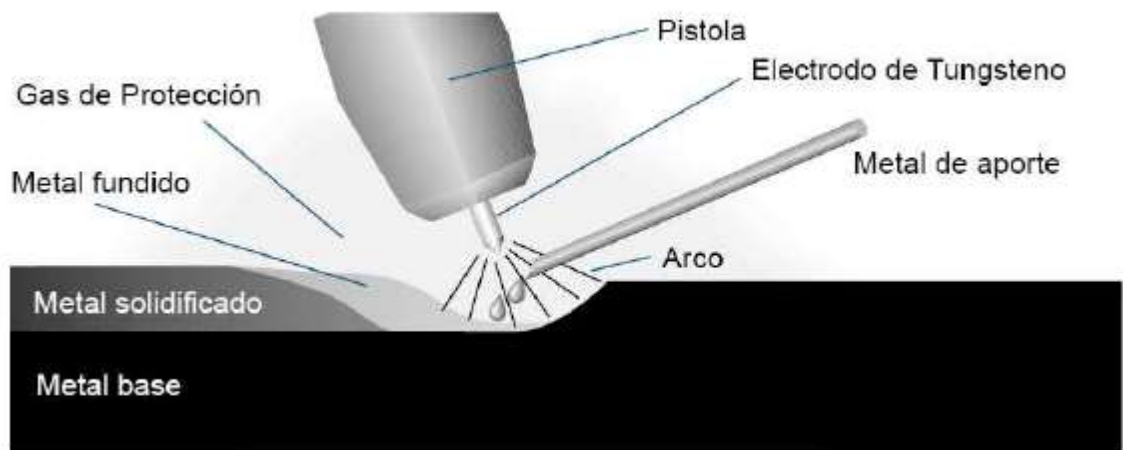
Diagrama esquemático del proceso de soldadura GTAW/TIG
